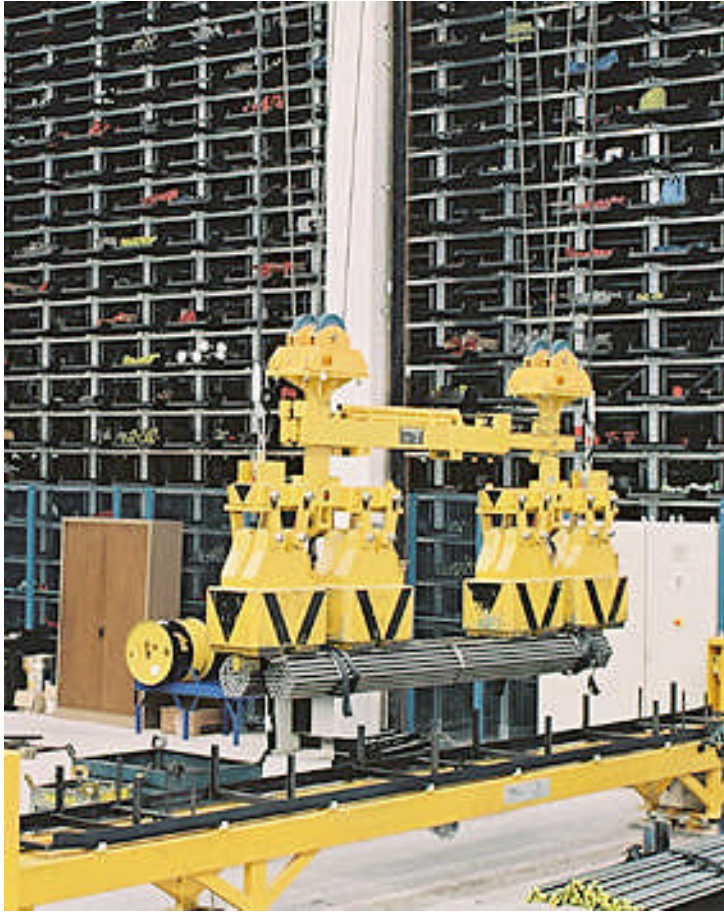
Zwei Stabstahlbunde werden in eine Lagerkassette abgelegt
